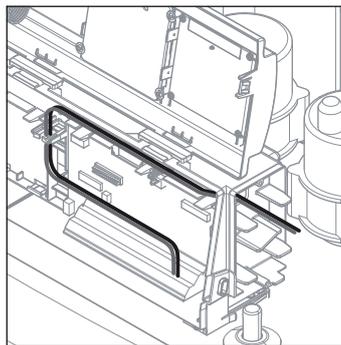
5. Posare i cavi nella regolazione e realizzare i collegamenti elettrici (vedere sezione 2.4.2).
